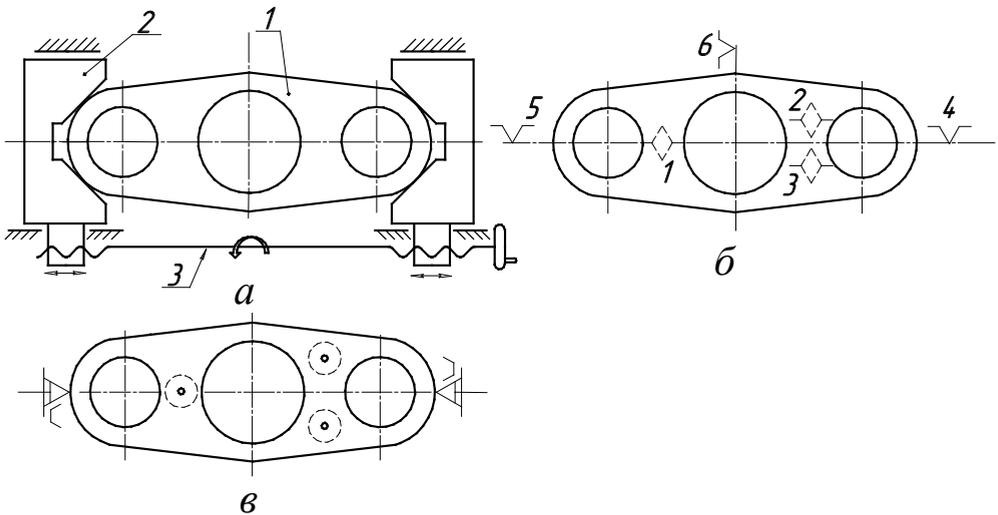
Установка заготовки в самоцентрирующих тисках
